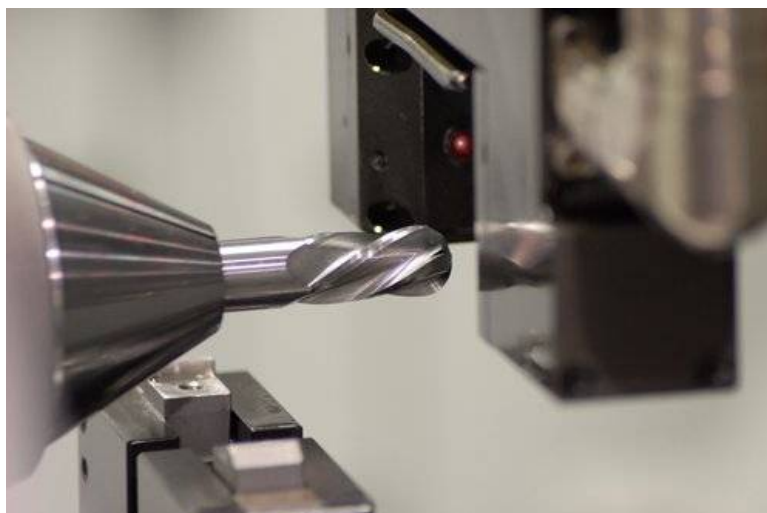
Изготовление уникального зенкера на шлифовально-заточном станке ANCA RX7
